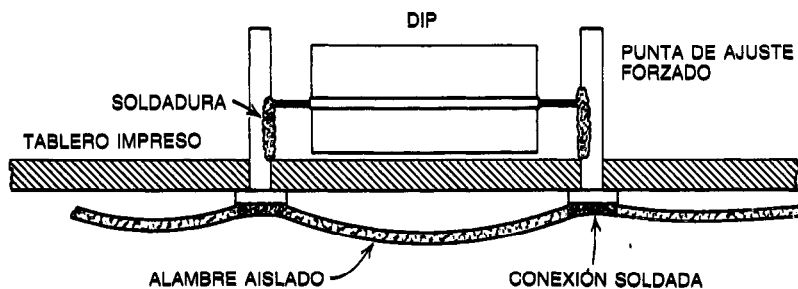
Conexiones por soldadura en puntas (soldadura por puntos).
